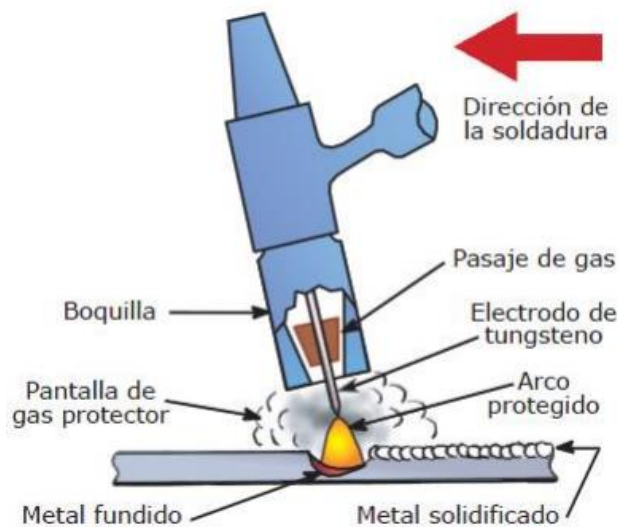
Proceso de soldadura GTAW o TIG [30].
